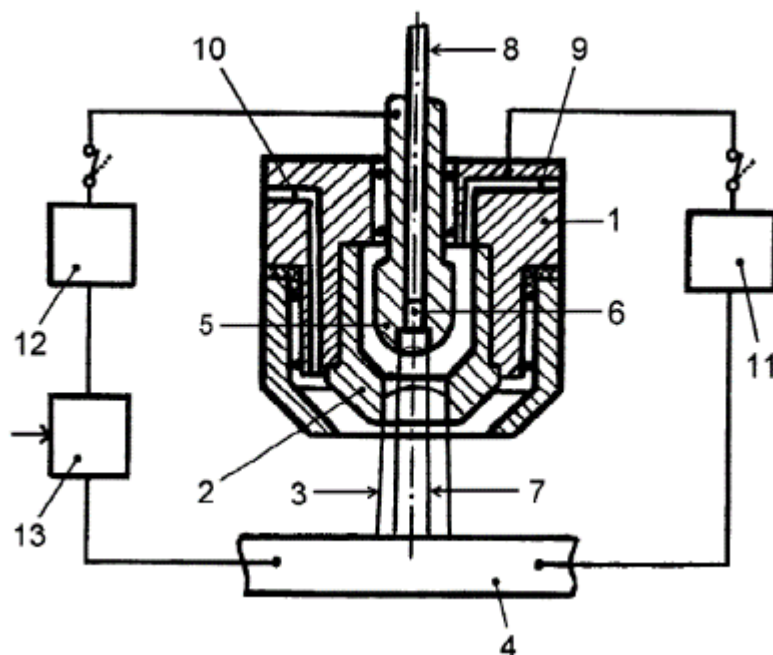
Схема плазменной сварки плавящимся электродом с пусковым неплавящимся электродом (1 – корпус; 2 – кольцевой неплавящийся электрод; 3 – сжатая дуга; 4 – свариваемое изделие; 5 – пусковой неплавящийся электрод; 6 – осевое отверстие; 7 – дуга между 5 и 4; 8 – плавящийся электрод; 9 – канал для плазмообразующего газа; 10 – канал для защитного газа; 11,12 – источники питания постоянного тока; 13 – осцилятор)
